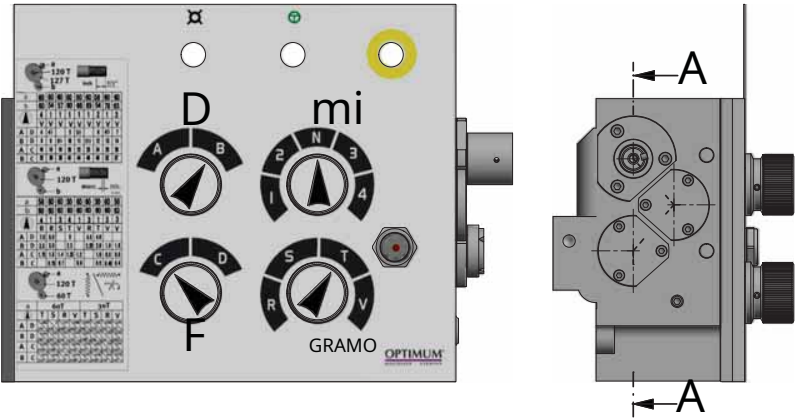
Vorschubgetriebe 1-6 - Engranaje de alimentación 1-6
